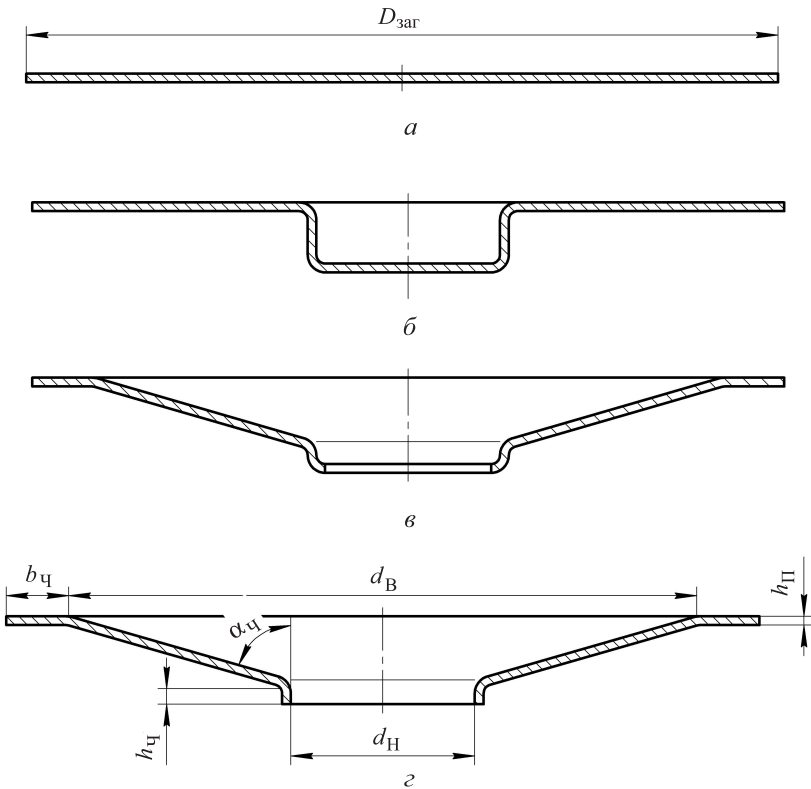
Последовательность операций листовой штамповки фильтроэлемента:
